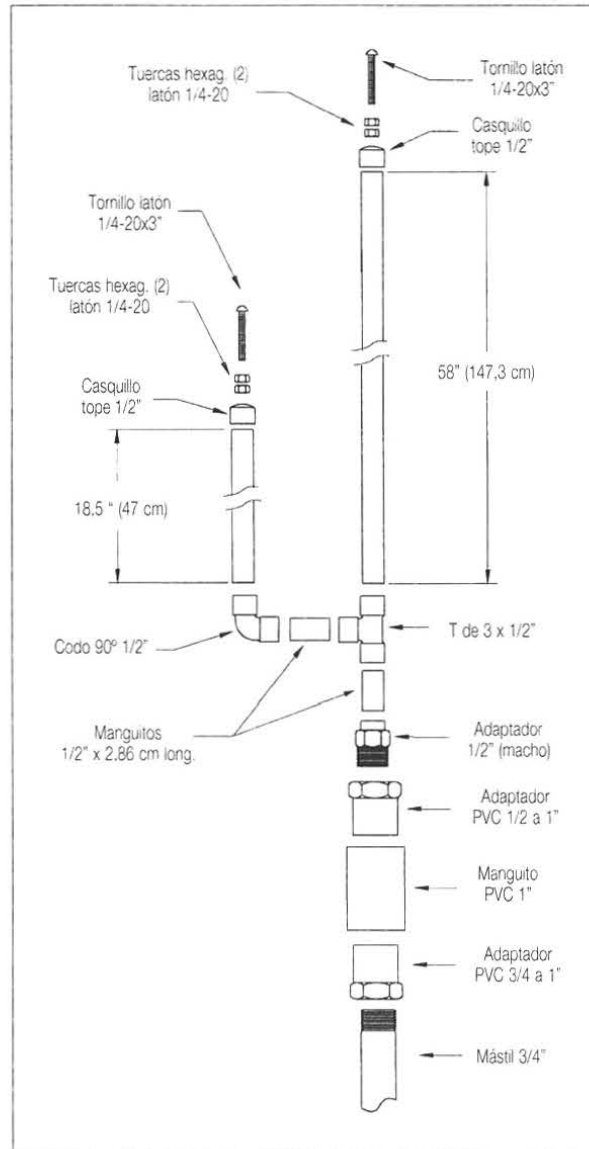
Croquis de despiece y dimensiones de una antena J para 2 metros.
